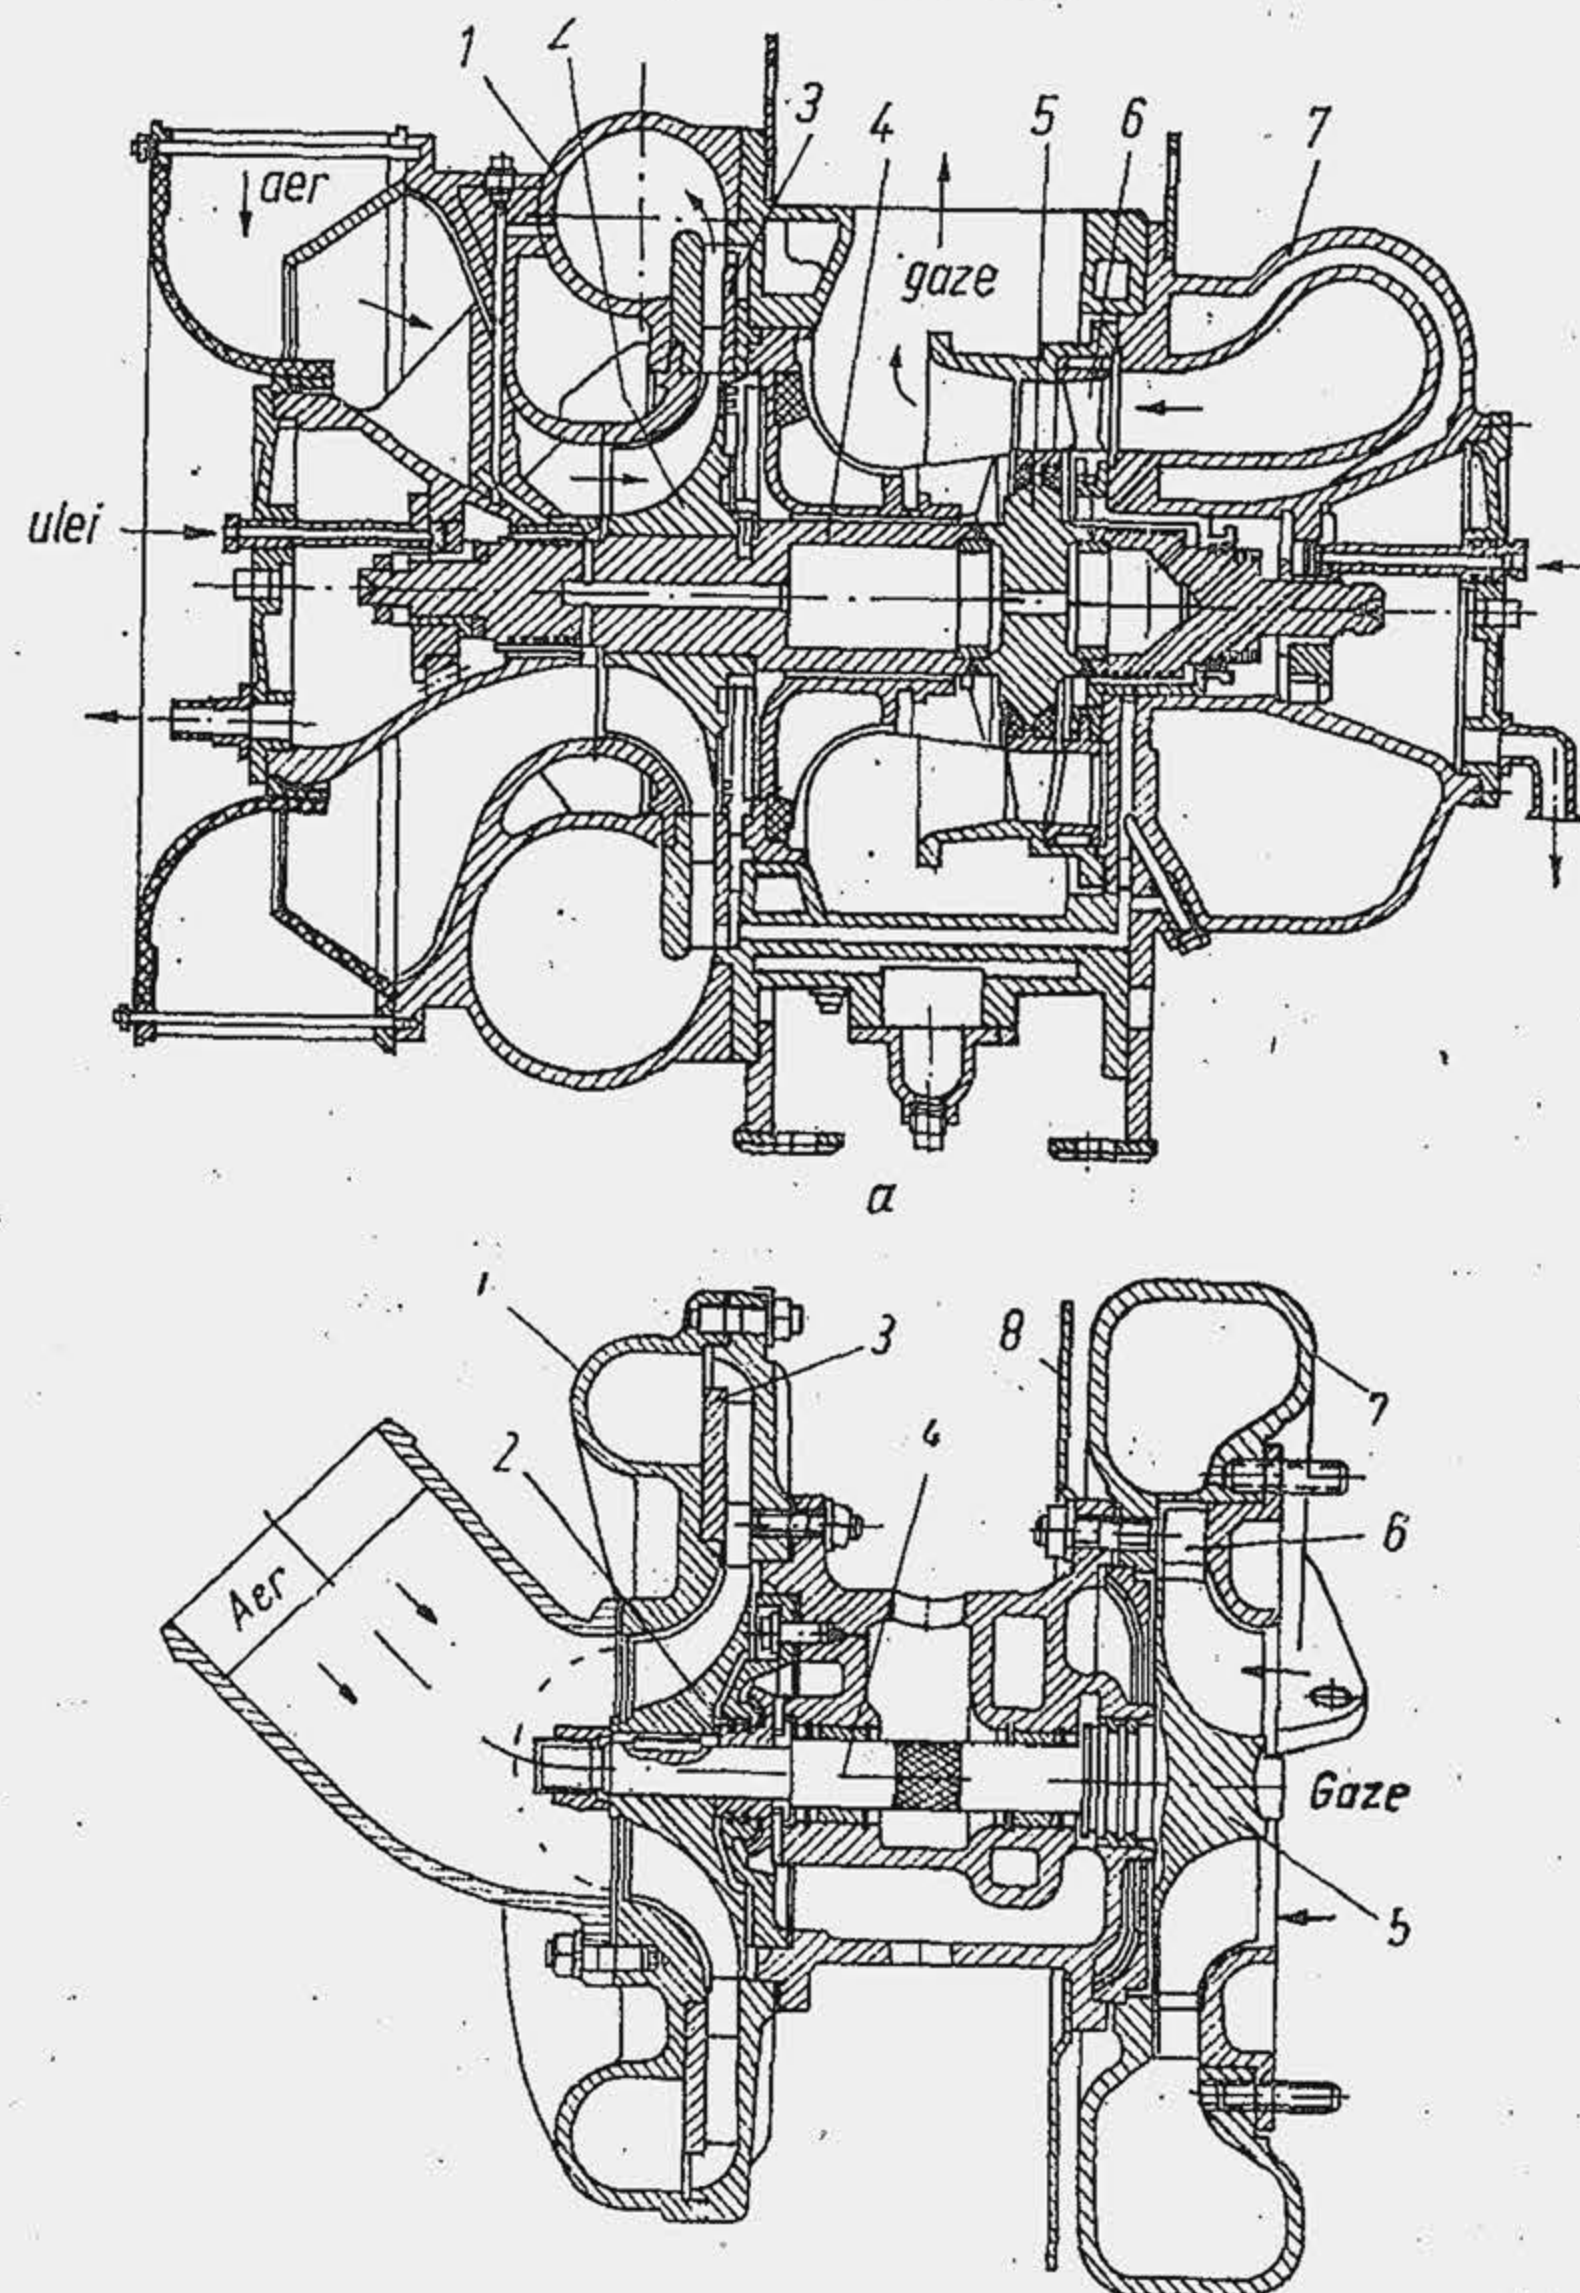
Turbosuflanta TK 30 cu turbină axială (a); turbosuflanta TKR-13 cu turbină radial-axială (b);
